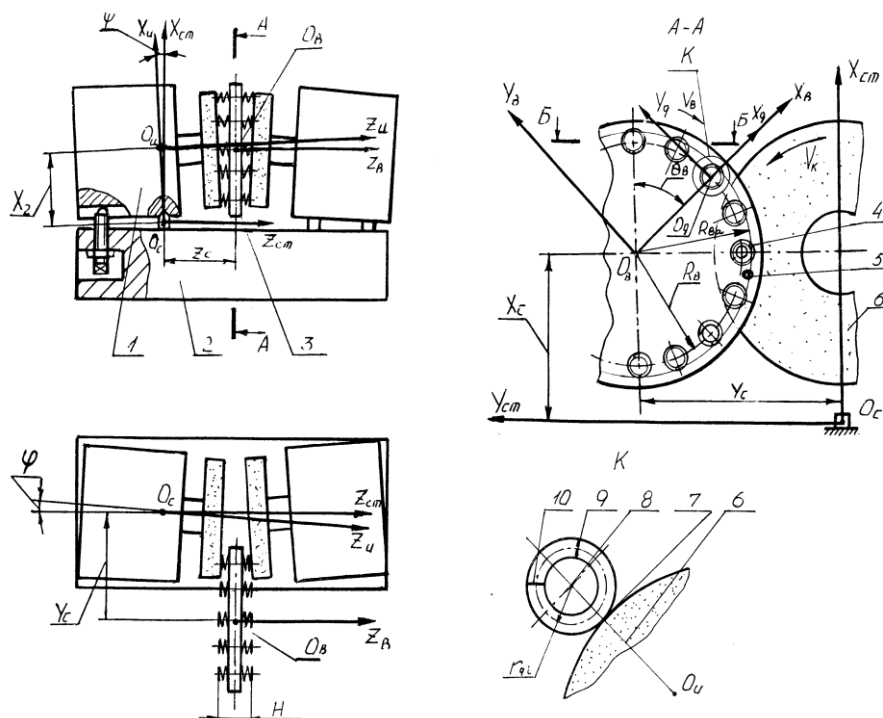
Формообразующая система двустороннего торцешлифовального станка
